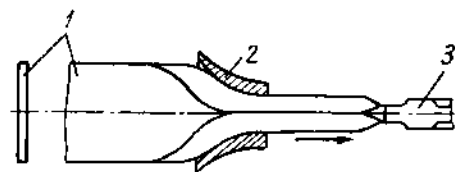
Схема процесса получения труб сваркой встык
